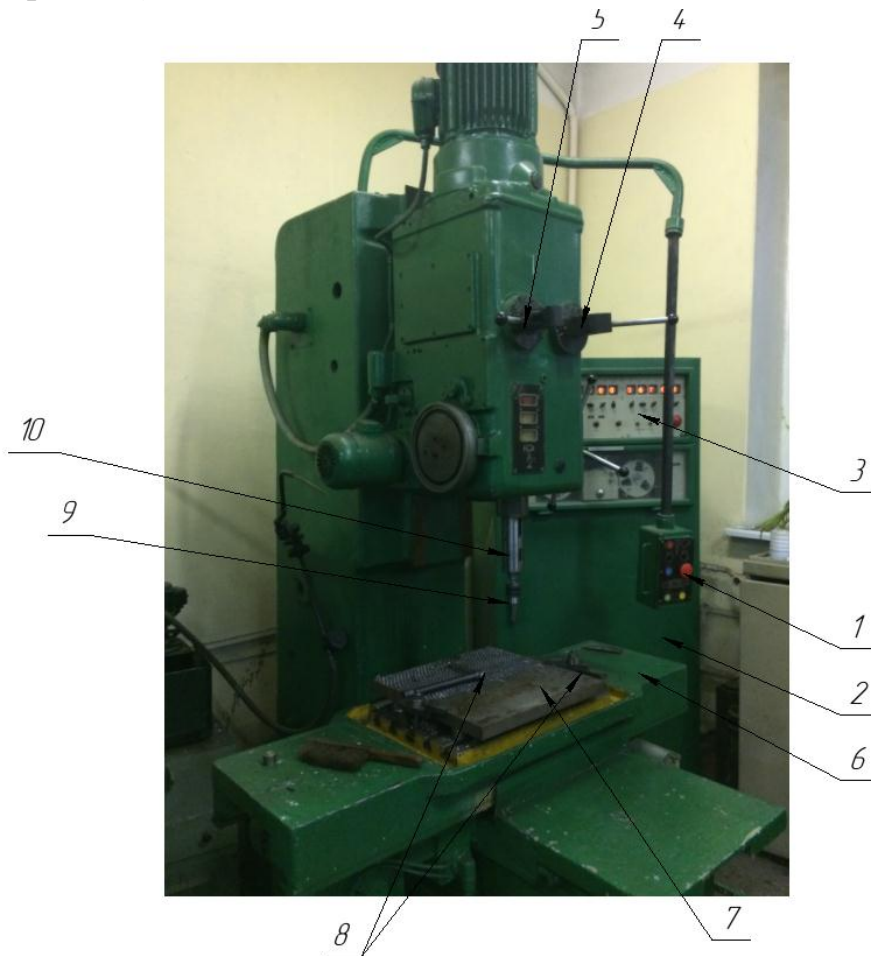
Зовнішній вигляд вертикально-свердлильного верстату
